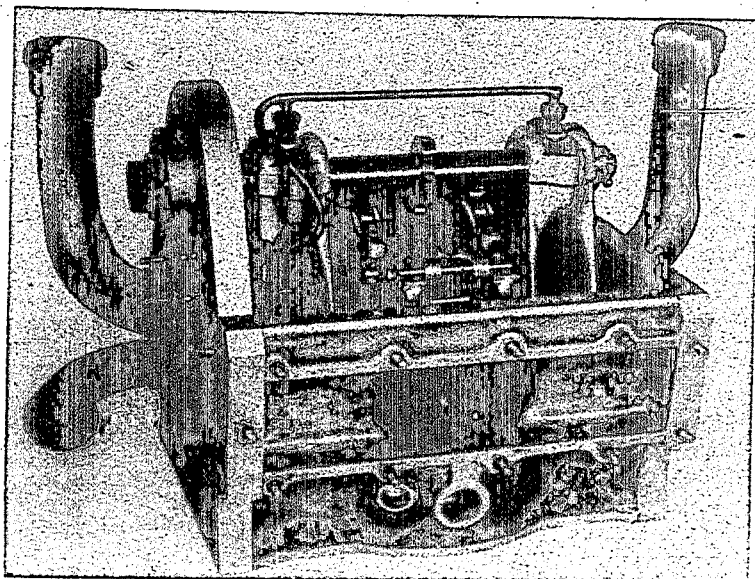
Zylinderkopf des I.G.-Versuchsmotors mit
